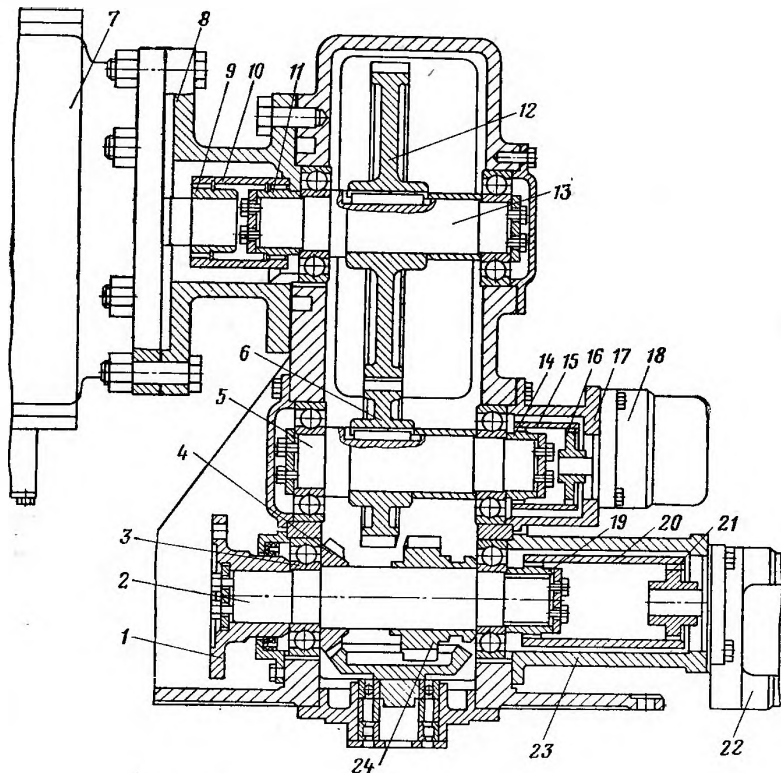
Редуктор насосов экскаватора ЭТР253
